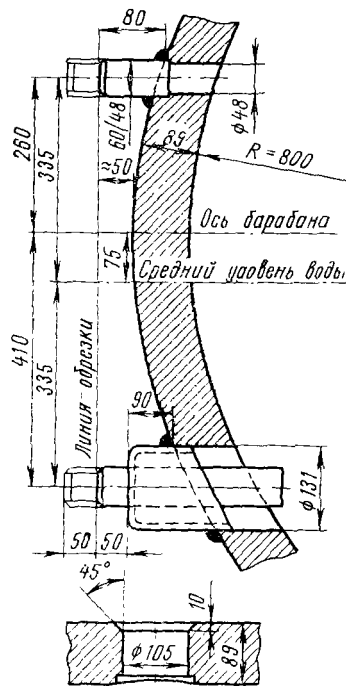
Сварные узлы барабана котла ТП-42: приварка штуцеров
